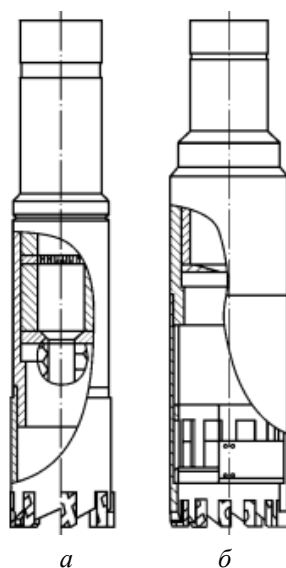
Фрезеры-ловители магнитные конструкции ЗАО «Завод „ИЗМЕРОН“»: а – типа ФЛМ; б – типа ФМЗ с механическим захватом
